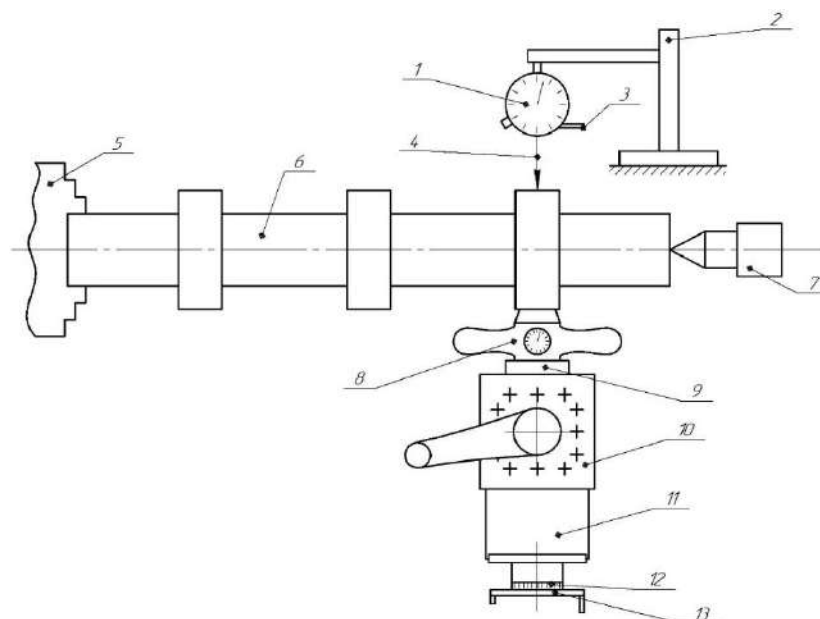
Измерительная установка: 1 – индикатор для измерения отжатый с корректирующим устройством; 2 – стойка индикатора на магнитном основании; 3 – отводка; 4 – иголка индикатора; 5 – трехкулачковый патрон; 6 – оправка; 7 – центр в пиноли задней бабки; 8 – пружинный динамометр ДС-0,2 с индикатором стрелочного типа; 9 – приспособление для закрепления динамометра в резцедержателе; 10 – резцедержатель; 11 – верхние резцовые салазки; 12 – лимб верхних резцовых салазок; 13 – рукоятка.
